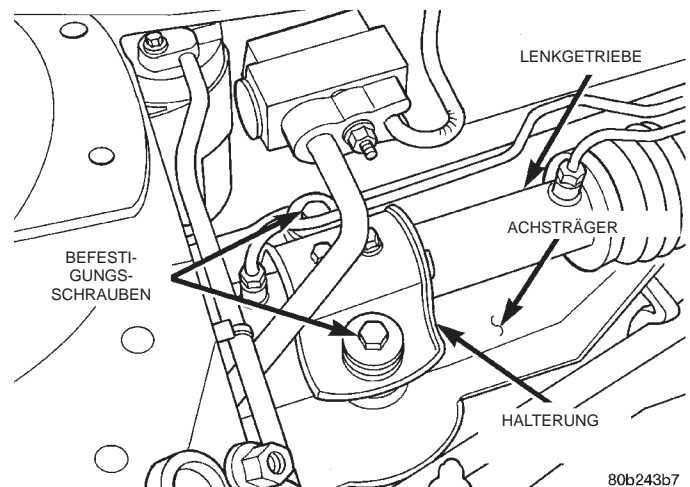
Befestigung des Lenkgetriebes am Achsträger (rechte Seite)
